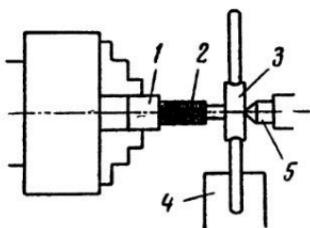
Нарезание резьбы метчиком на токарном станке: 1 — обрабатываемая деталь; 2 — метчик; 3 — вороток; 4 — суппорт; 5 — центр задней бабки.
